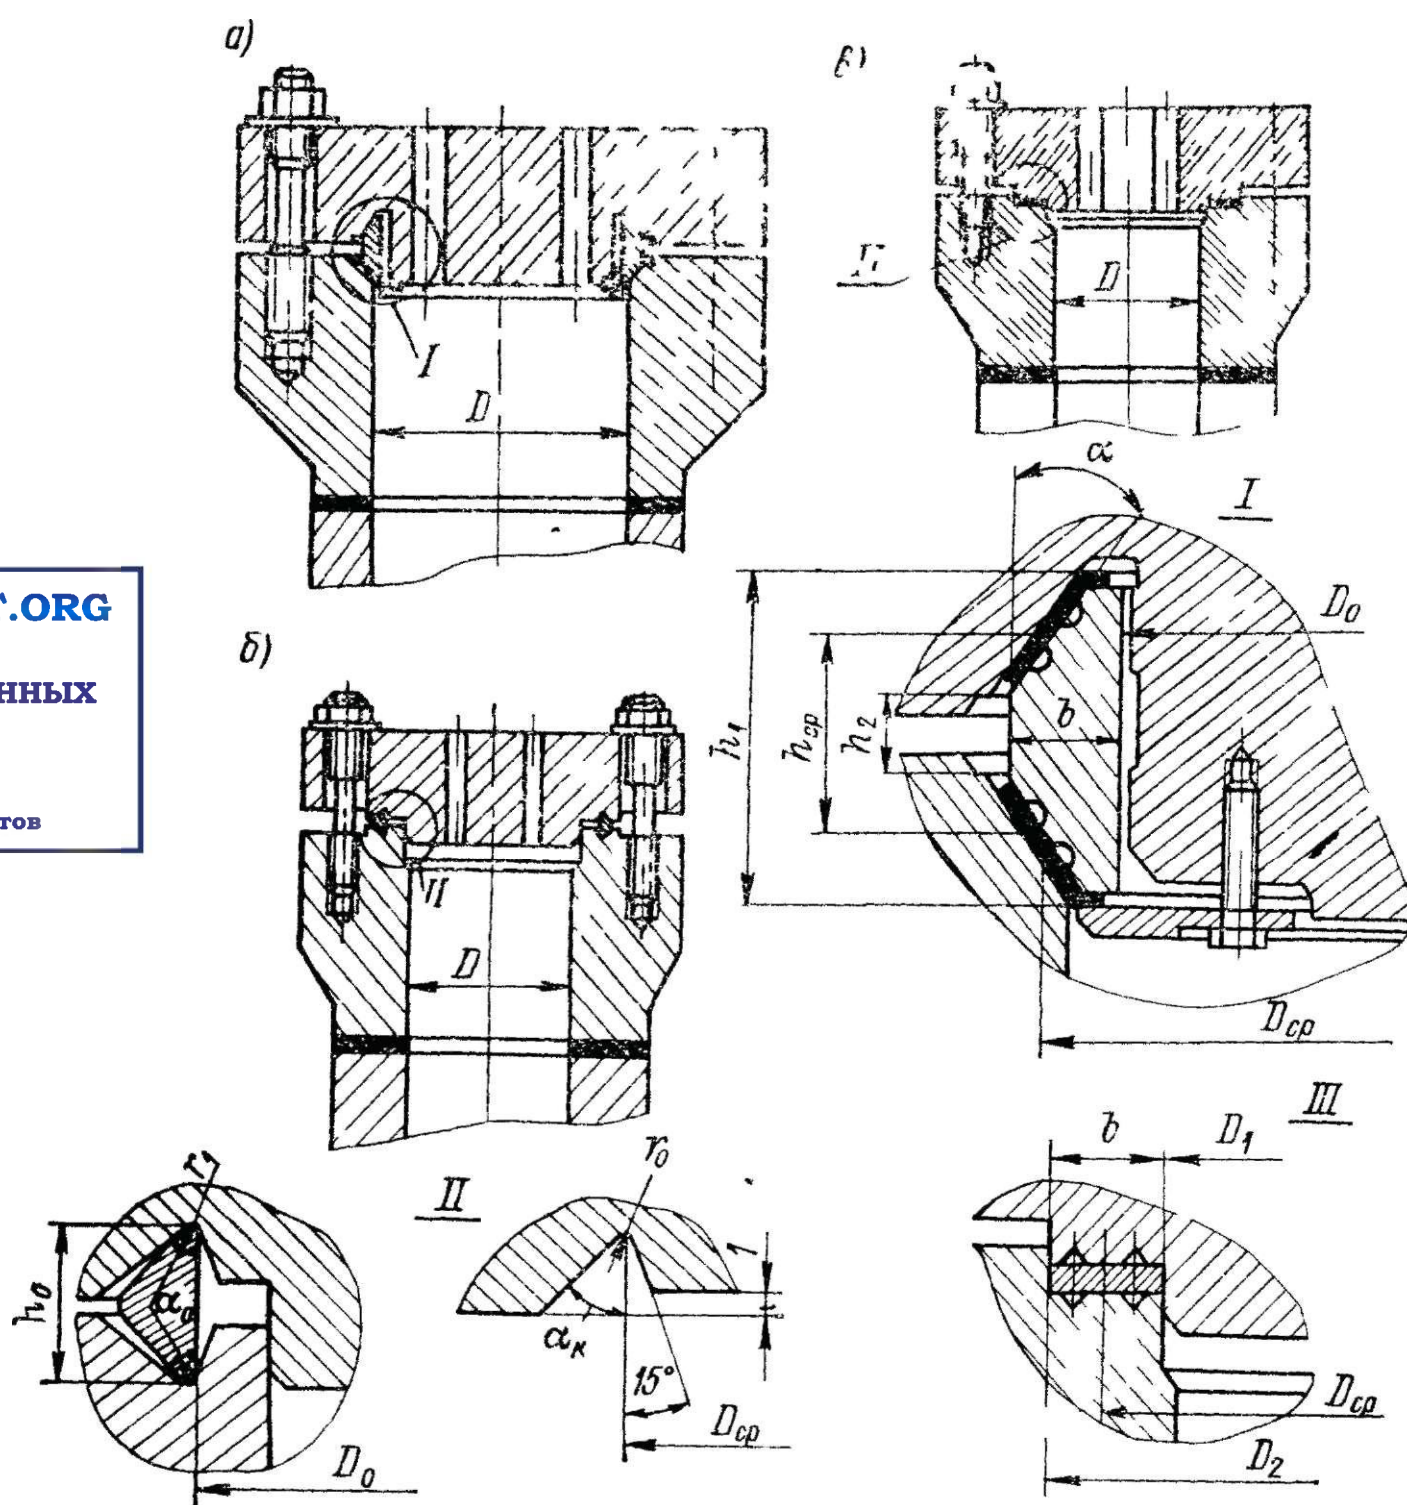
Конструкции затворов а — с двухконусным obtюратором, б — с дельта-obтюратором; в — с плоской металлической прокладкой
